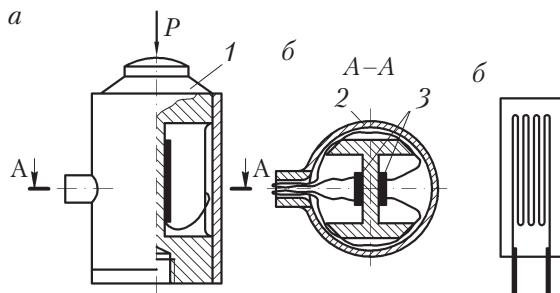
Тензорезисторный измерительный преобразователь больших сил
